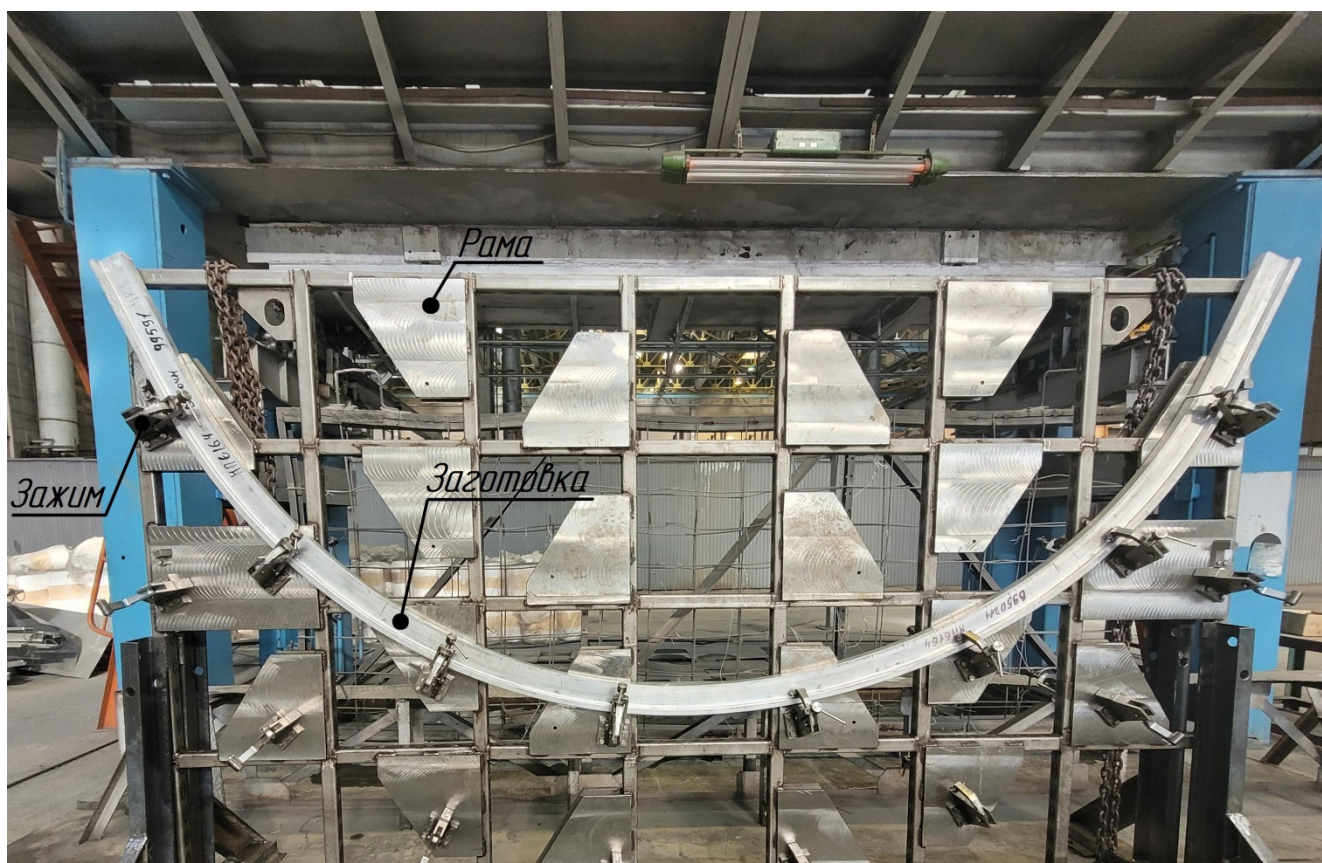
Заготовка сегмента шпангоута, закрепленная в приспособлении для термофиксации.
